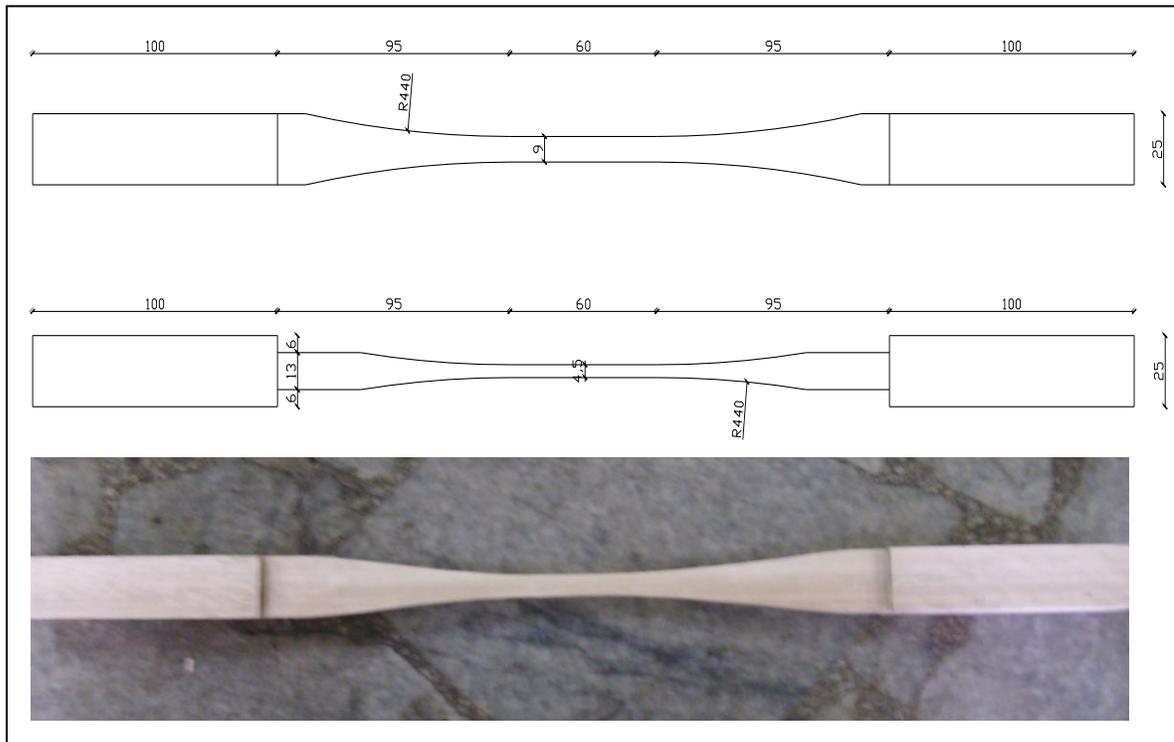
Probeta para ensayo de tracción paralela, en mm.
